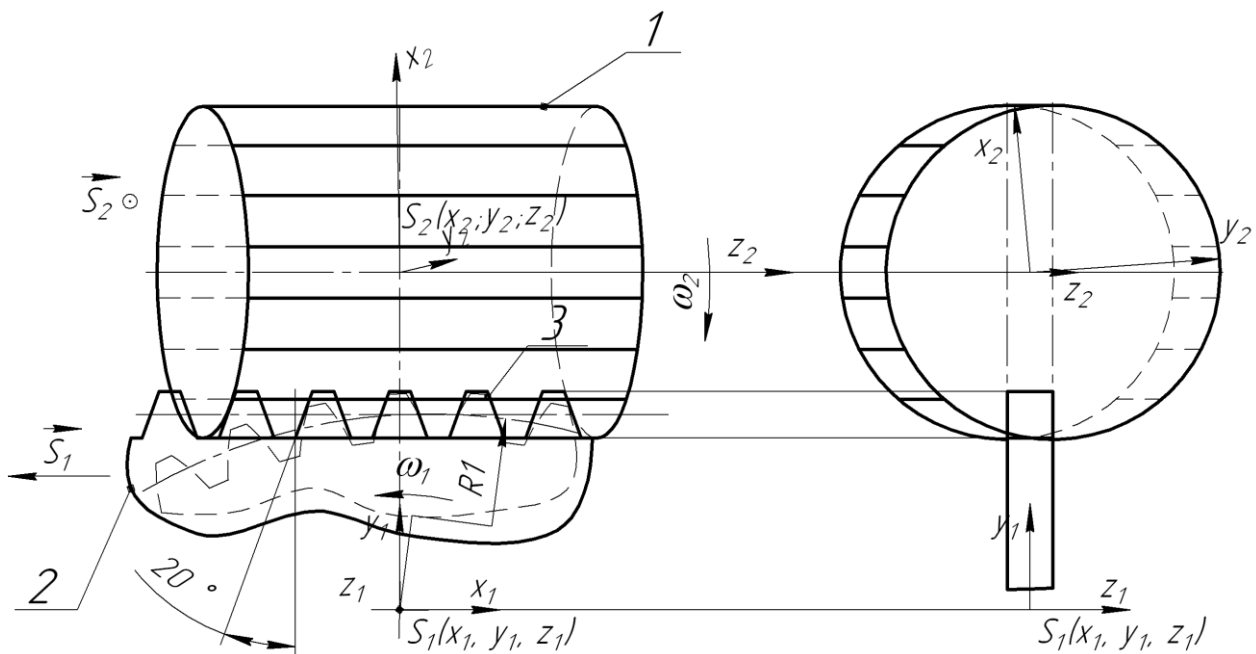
Схема формообразования цилиндрического зубчатого колеса гиперboloидным шлифовальным кругом
